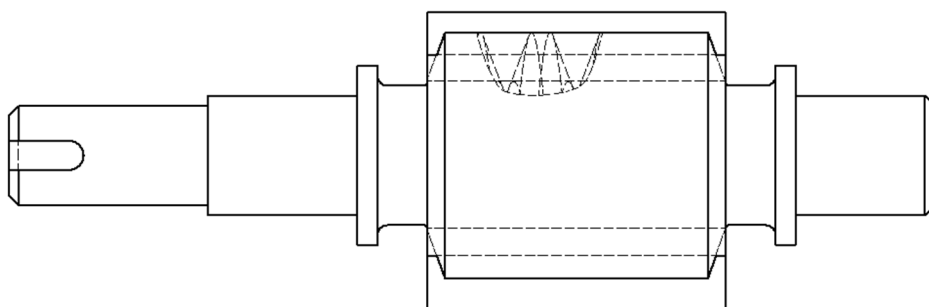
2-й місцевий розріз, деталі – циліндричний черв'як та оболонка циліндричного черв'яка
